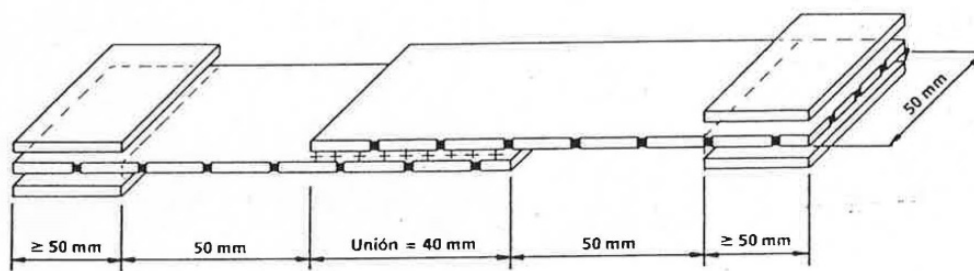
Probeta para ensayar la soldadura por tracción
